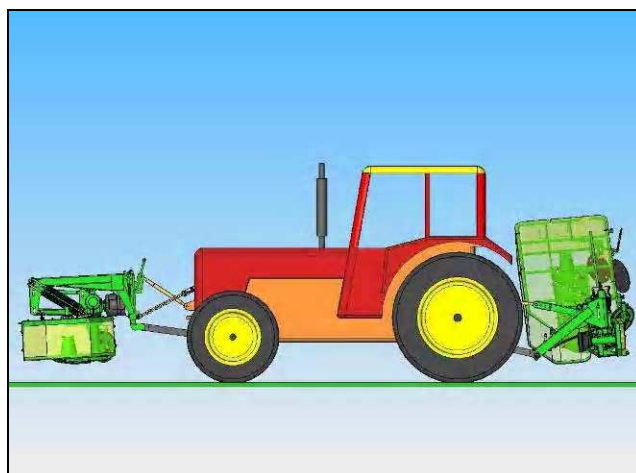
б. Косилки KDF и KDT в положении для поворотов.
